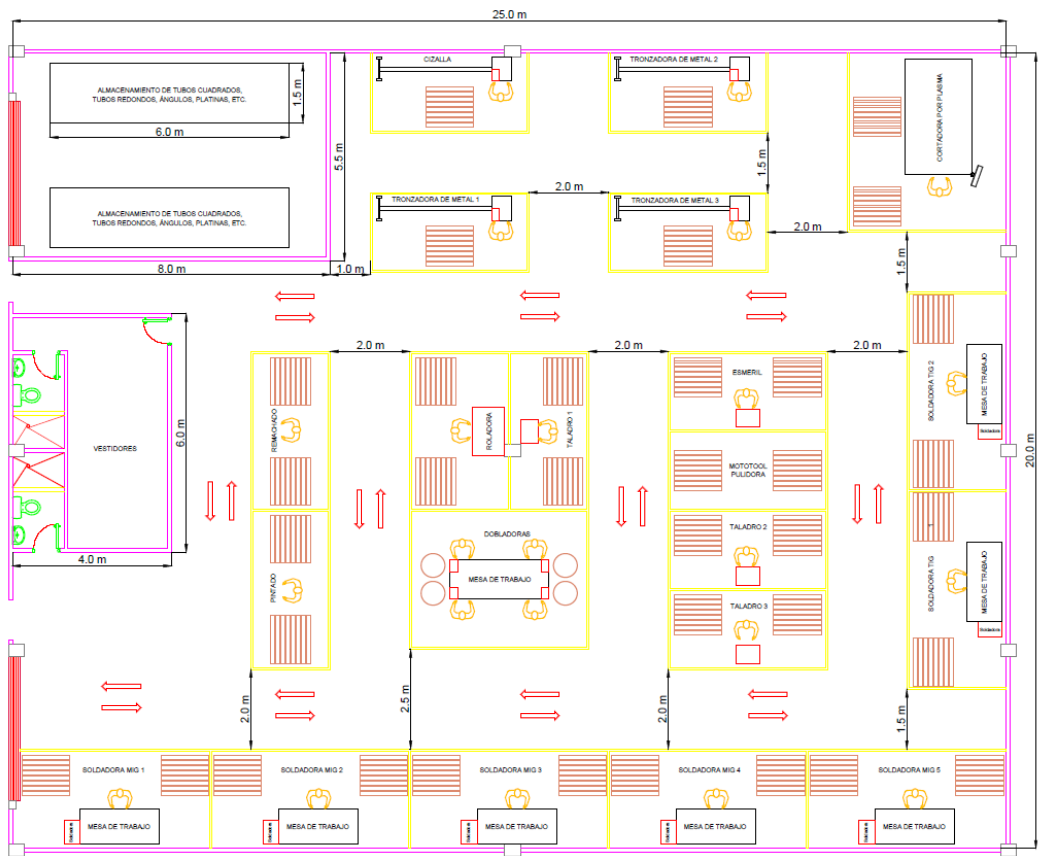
Opción 2 de Layout realizado en AutoCAD de 500 m². Fuente: Autor.
